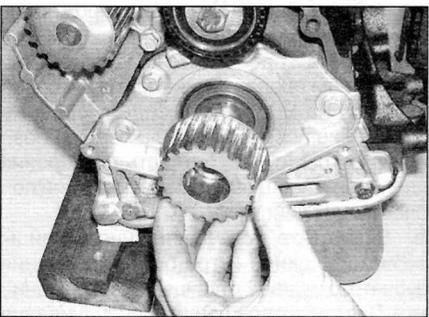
, а. Снимите зубчатый шкив с коленчатого вала...
